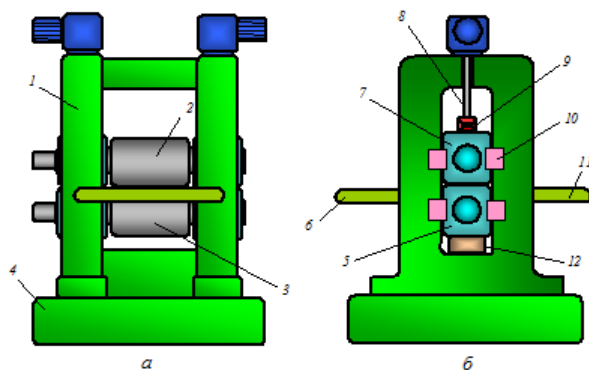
Рабочая клетка: *а* – вид спереди; *б* – вид сбоку; 1 – станина; 2, 3 – верхний и нижний рабочие валки; 4 – плитовина; 5, 7 – нижняя и верхняя подушки; 6, 11 – входной и выходной столы с линейками; 8 – нажимное устройство; 9 – предохранительное устройство; 10 – устройство осевой установки и фиксации валков; 12 – устройство уравнивания валков
